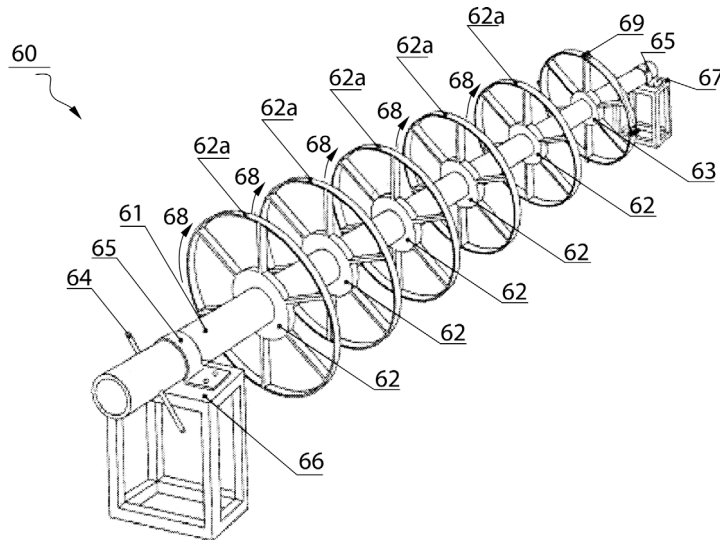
Вид в аксонометрии каркаса приспособления для внекорпусной сборки поперечного набора и его соединения с трехслойной оболочкой
